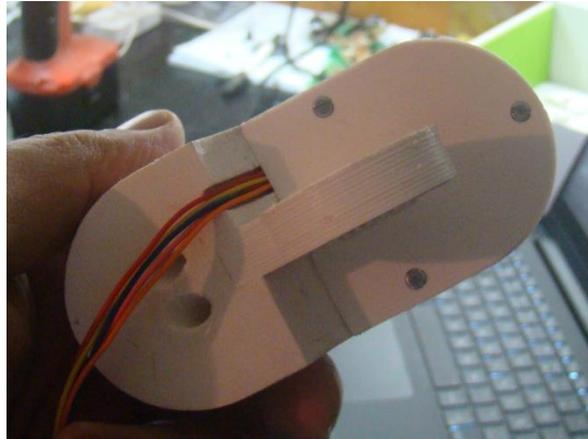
Tampa inferior traseira do núcleo de suporte do motor colocada. Reparar no detalhe da passagem dos fios do motor de passo por dentro do rebaixo no plástico.
